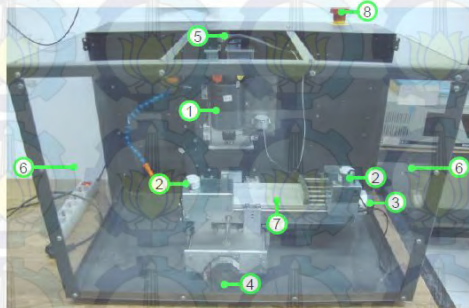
Mesin CNC Mill Package 35-005-C
